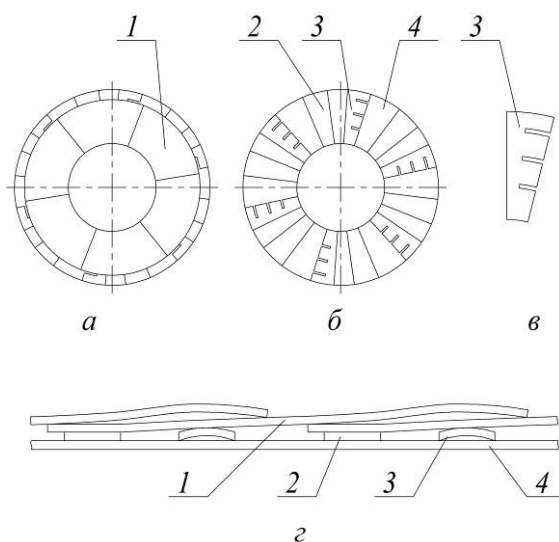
Лепестковый газодинамический подшипник осевой TFGB44.
